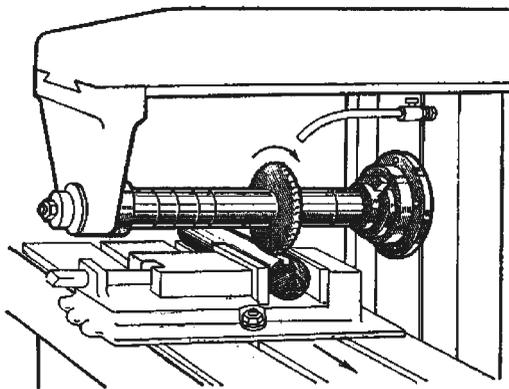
Фрезерование открытого шпоночного паза с установкой вала в тисках
